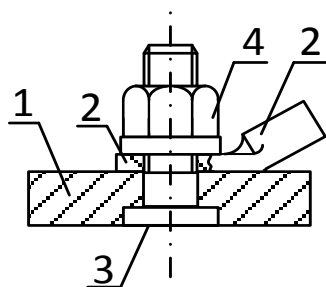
Контактное соединение шин ШУП-МДР (1 - медная шина; 2 – кабельный наконечник; 3 – винт запрессовочный; 4 – гайка с зубчатым фланцем).
